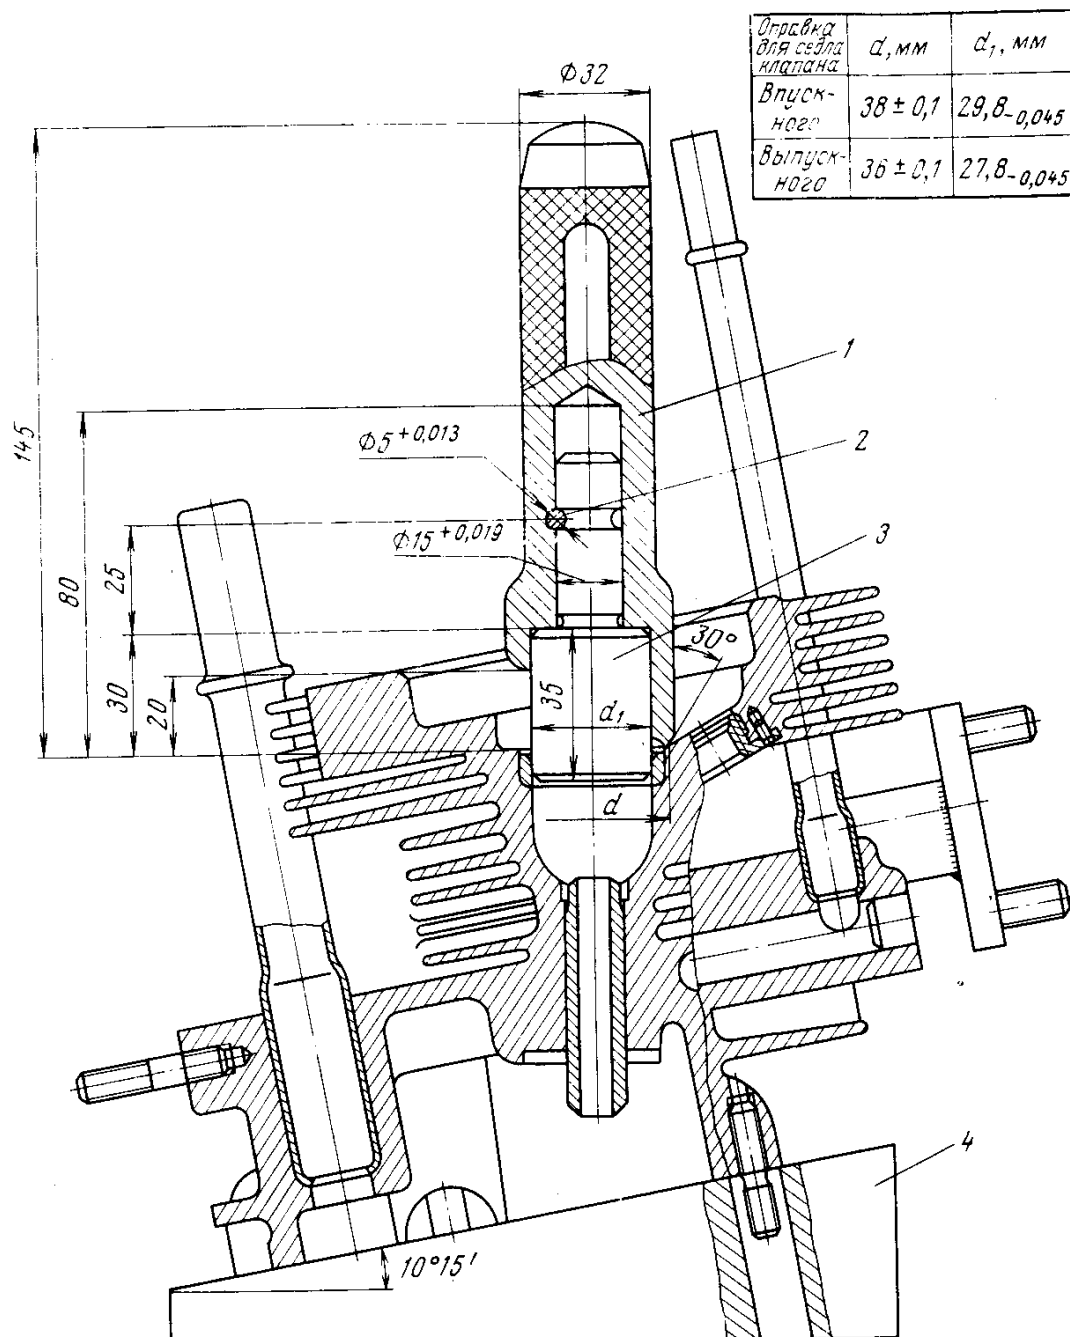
Оправка для зачеканивания седла клапана: 1—корпус; 2—штифт; 3—вставка; 4—подставка
